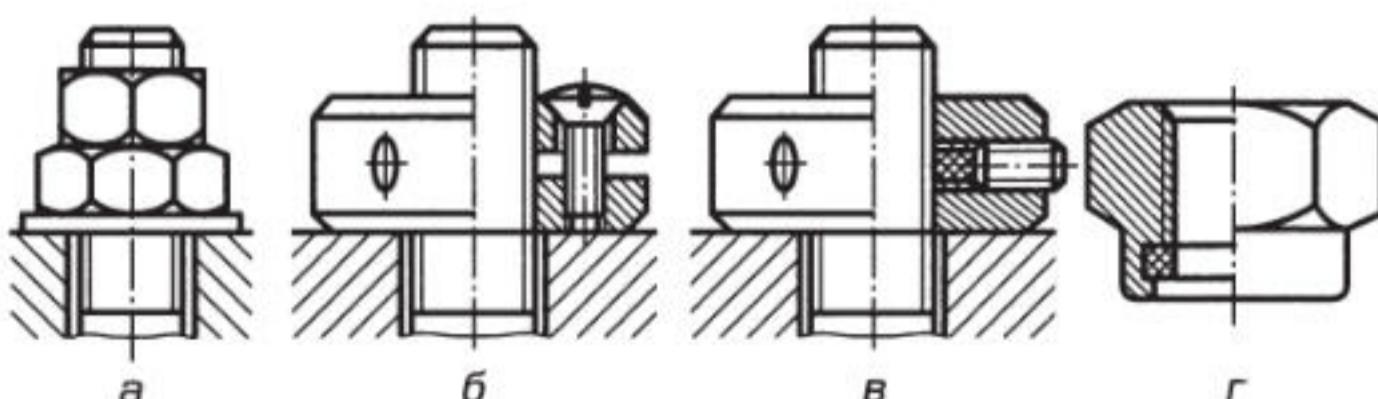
Резьбовые соединения с предохранением от самоотвинчивания дополнительной резьбовой деталью:
